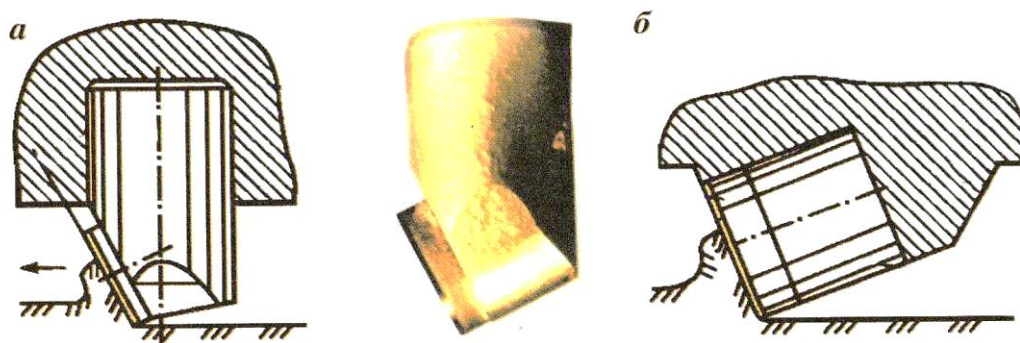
Крепление алмазно-твердосплавной пластинки: а – алмазно-твердосплавный зубок; б – алмазно-твердосплавный резец
